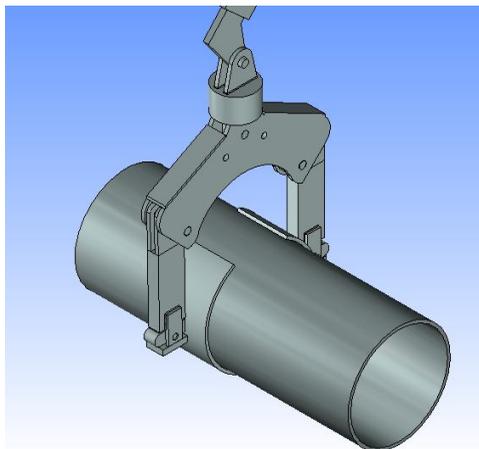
Параметрическая сборочная 3d-модель грузозахватного устройства
